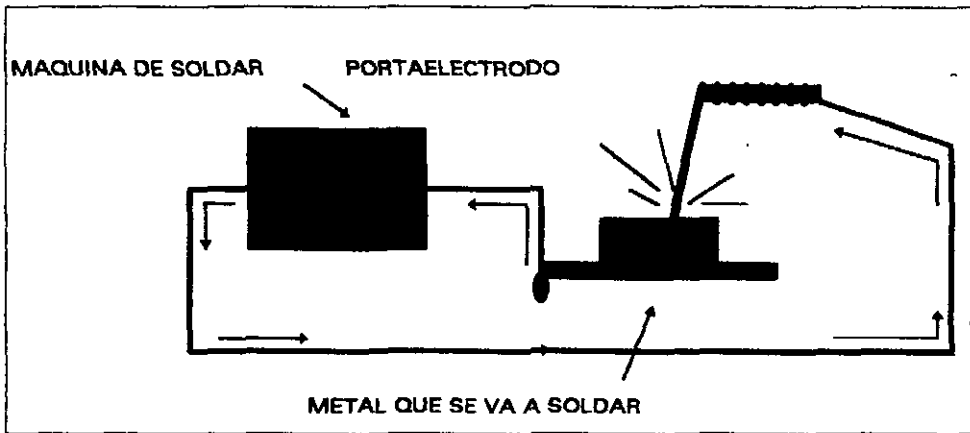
EL CIRCUITO DE SOLDADURA.
